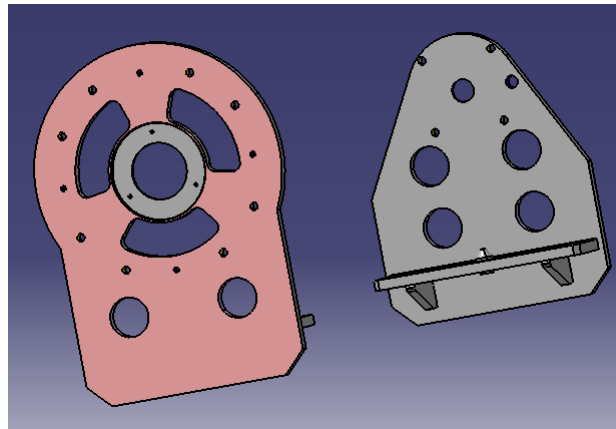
Placas de amarre del utillaje al motorreductor del posicionador. A la izquierda: punto (lado motriz) y a la derecha: contrapunto. Fuente: Interob (2014).
